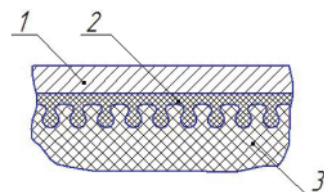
Схема скрепления заряда твердого топлива с корпусом газогенератора: 1 – корпус; 2 – профильное теплозащитное покрытие; 3 – твердое топливо
